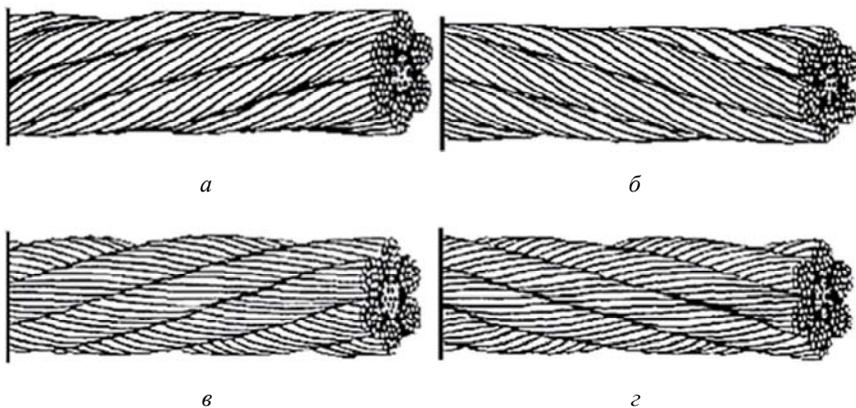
Схемы канатов двойной свивки по направлению свивки и по сочетанию направлений свивки каната и его прядей:
